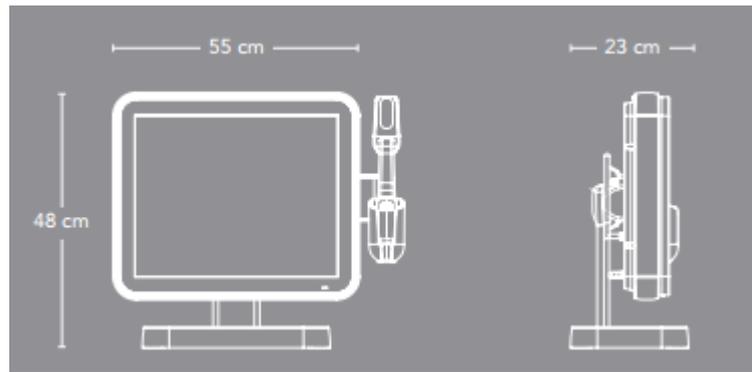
dimensions de la nouvelle version, à poser sur le plan de travail (18).
